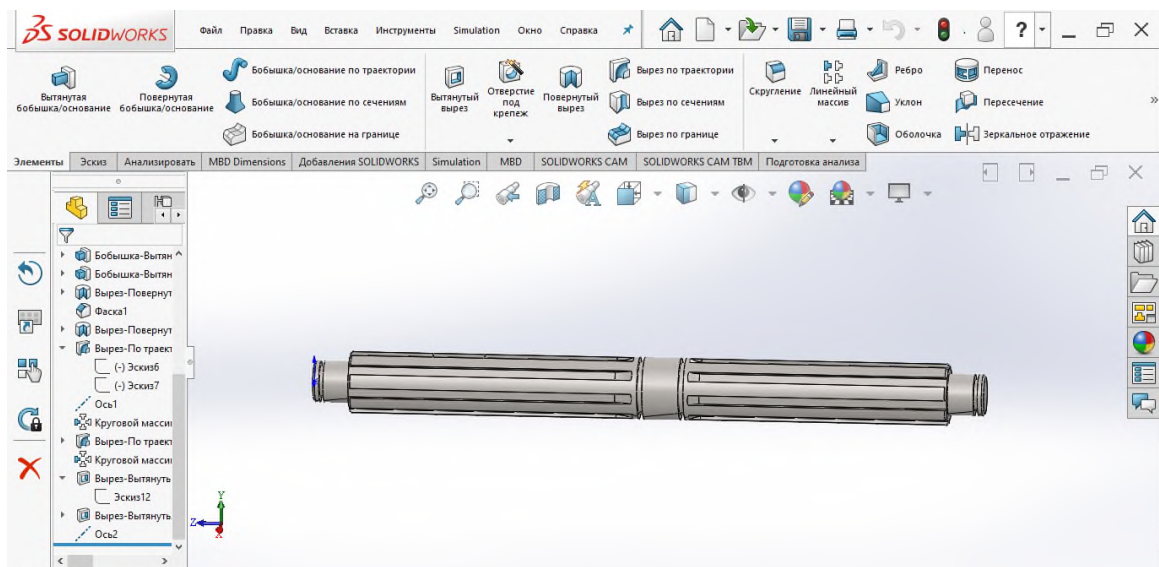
Твердотільна модель четвертого вала коробки швидкостей
